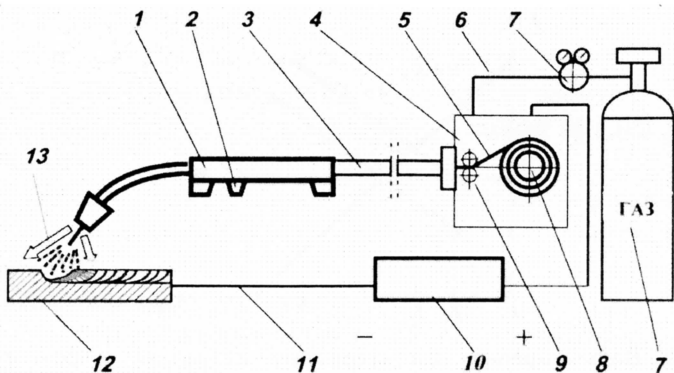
Схема полуавтомата для дуговой сварки в защитном газе: 1 – сварочная горелка; 2 – кнопка «Пуск»; 3 – шланг; 4 – механизм подачи проволоки; 5 – электродная проволока; 6 – газокоммуникации; 7 – газовая аппаратура; 8 – кассета; 9 – электрический привод; 10 – источник питания; 11 – электрокоммуникации; 12 – свариваемая заготовка; 13 – защитный газ
